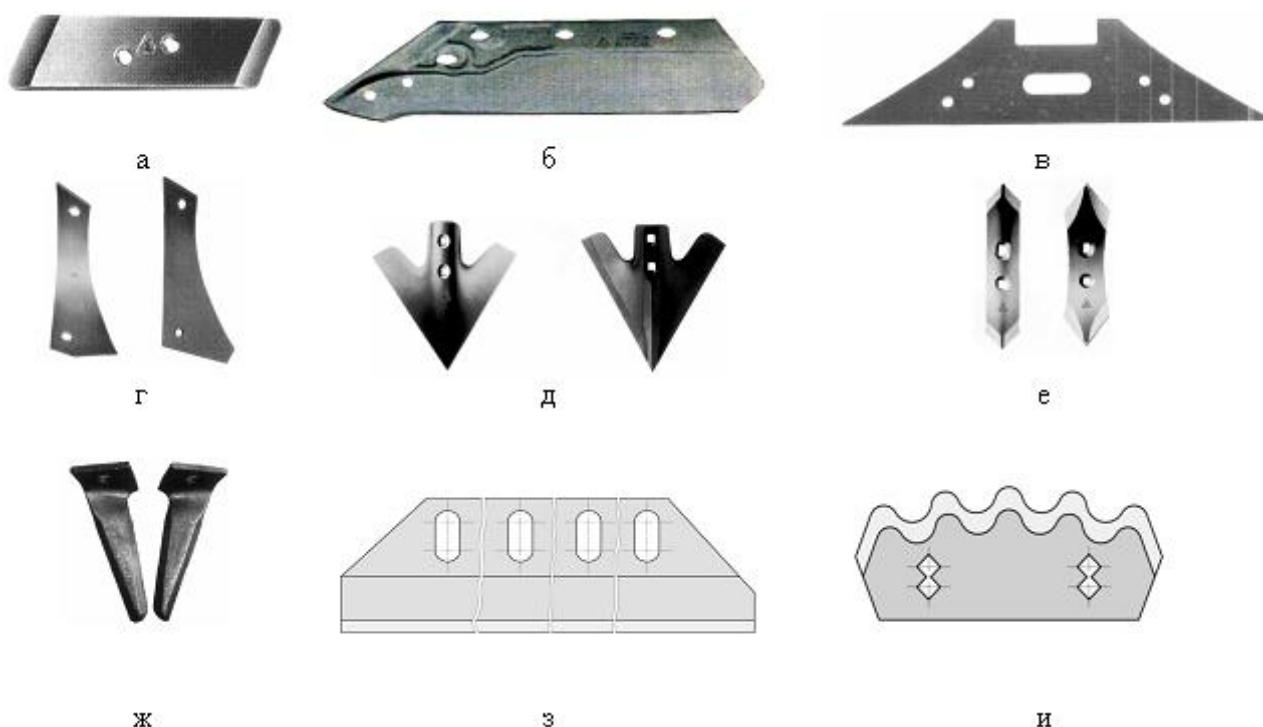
Типовые представители сменных ДРОМ почвообрабатывающих и кормоуборочных машин: а – долото; б – лемех; в – полевая доска; г – груды отвалов; д – стрельчатые лапы; е – оборотные лапы; ж – зубья роторных борон; з – нож измельчающего аппарата кормоуборочного комбайна; и – нож измельчителей рулонов
